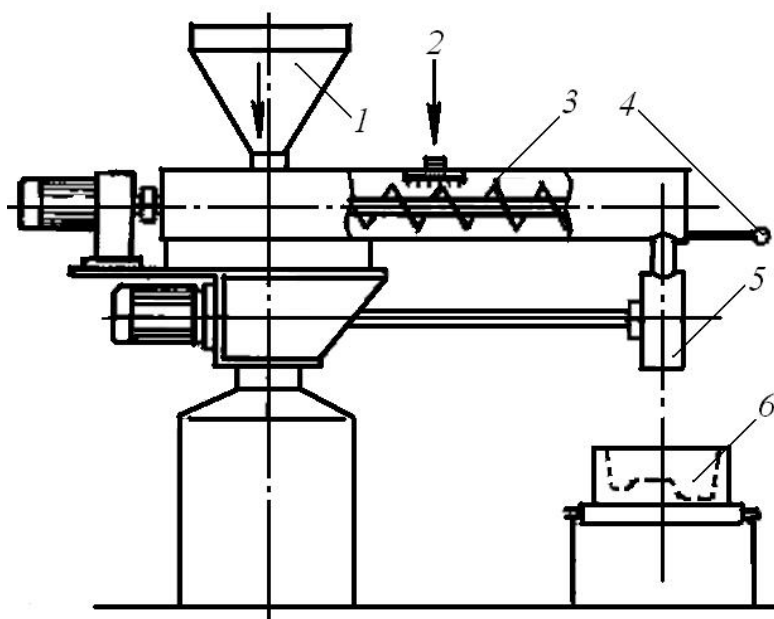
Компоновка миксер-слингера для набивки стержней из холоднотвердеющих смесей:
